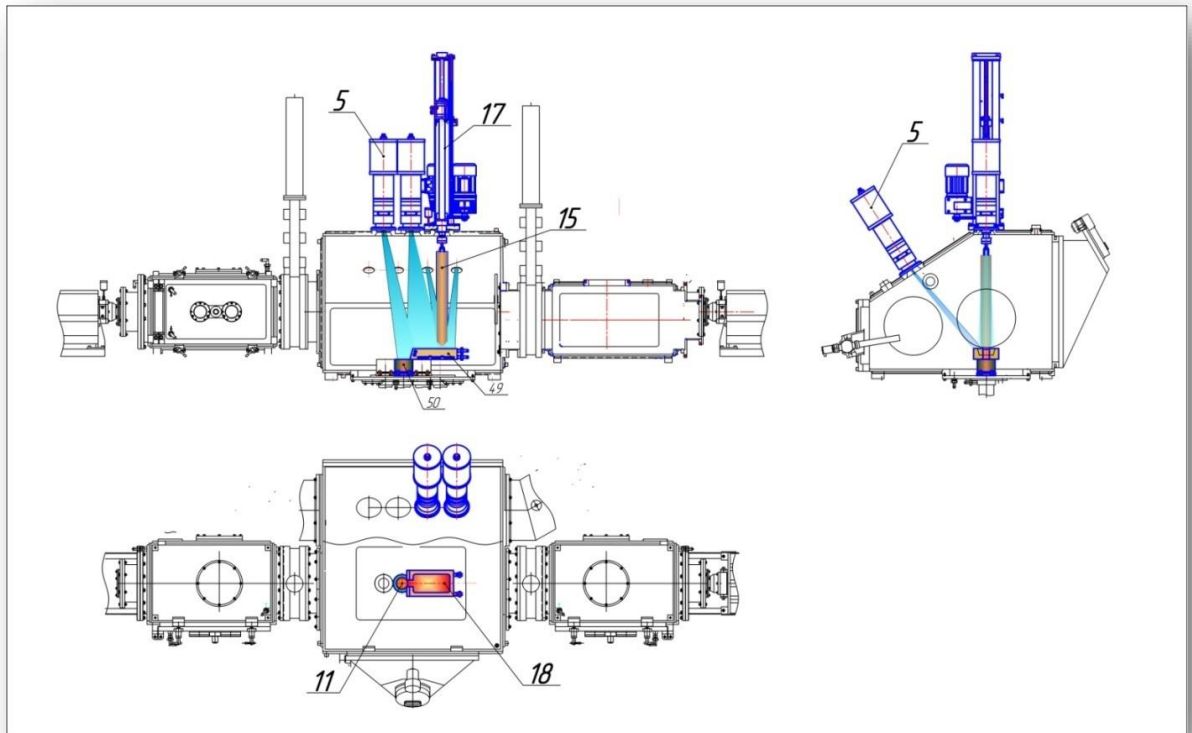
Схема переплаву заготовки в кристалізатор з використання проміжної ємності (5 – електронна гармата, 11 – кристалізатор, 15 – вертикальна заготовка, 17 – механізм підвіски заготовки, 18 – проміжна ємність)
